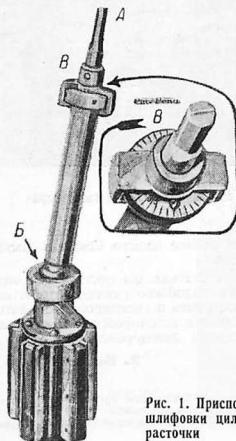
Приспособление для шлифовки цилиндров после расточки
